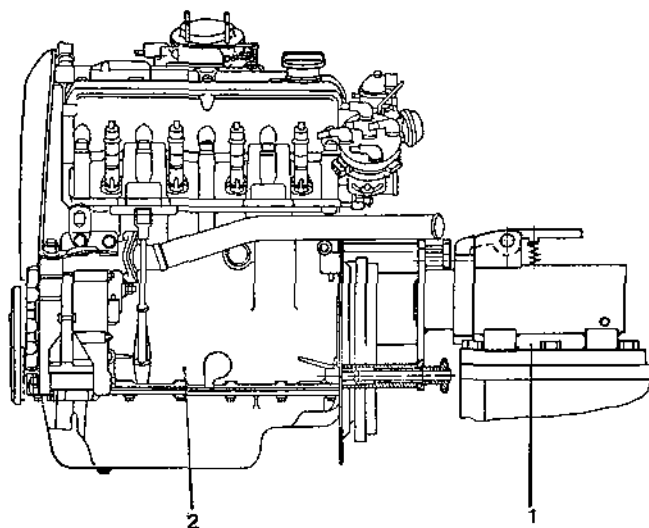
Двигатель, установленный на приспособление для разборки и сборки:
